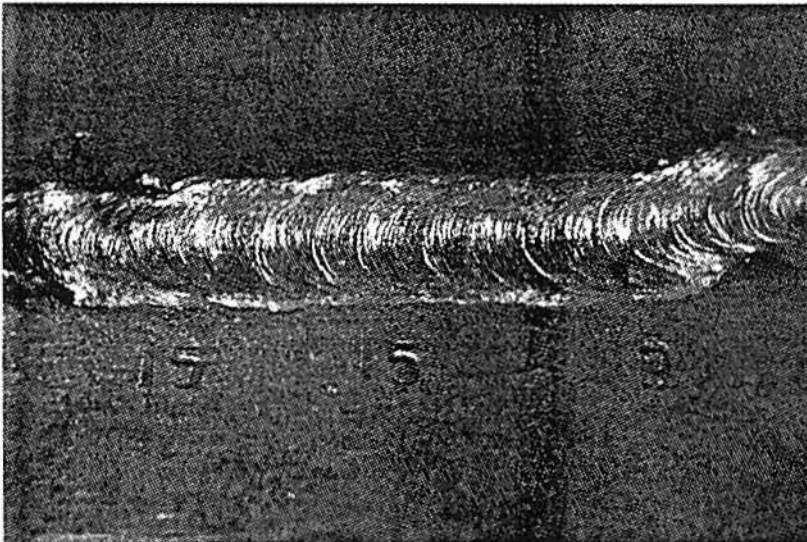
Juntas tipo filete, soldadas com a mistura Ca01.
